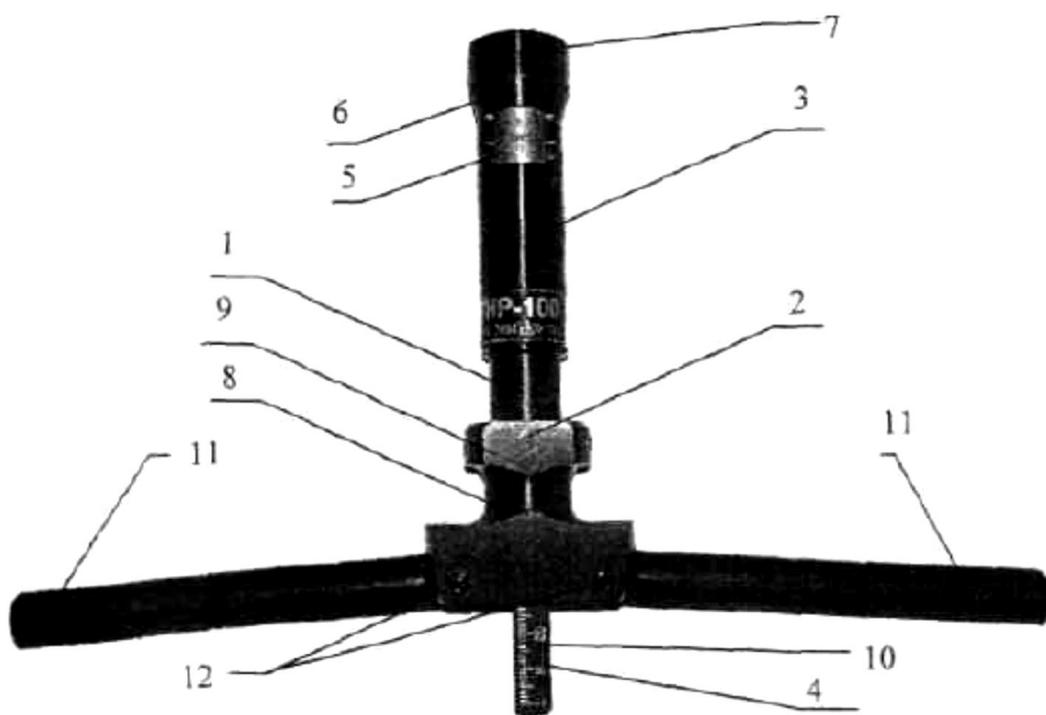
Прибор для проверки натяжения приводного ремня ППНР-100
